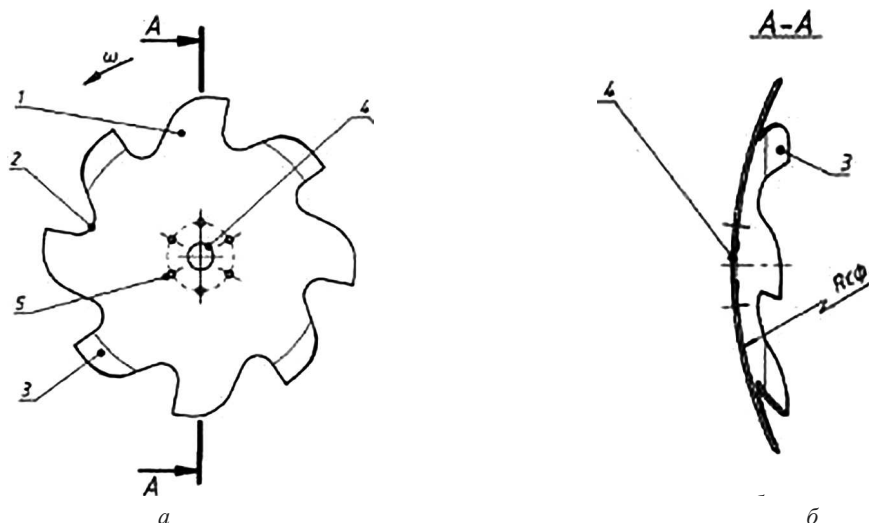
Схема сферического диска почвообрабатывающего орудия: а – вид сбоку; б – разрез А-А; 1, 3 – зубья; 2 – вырез; 4 – установочное отверстие; 5 – крепежное отверстие
